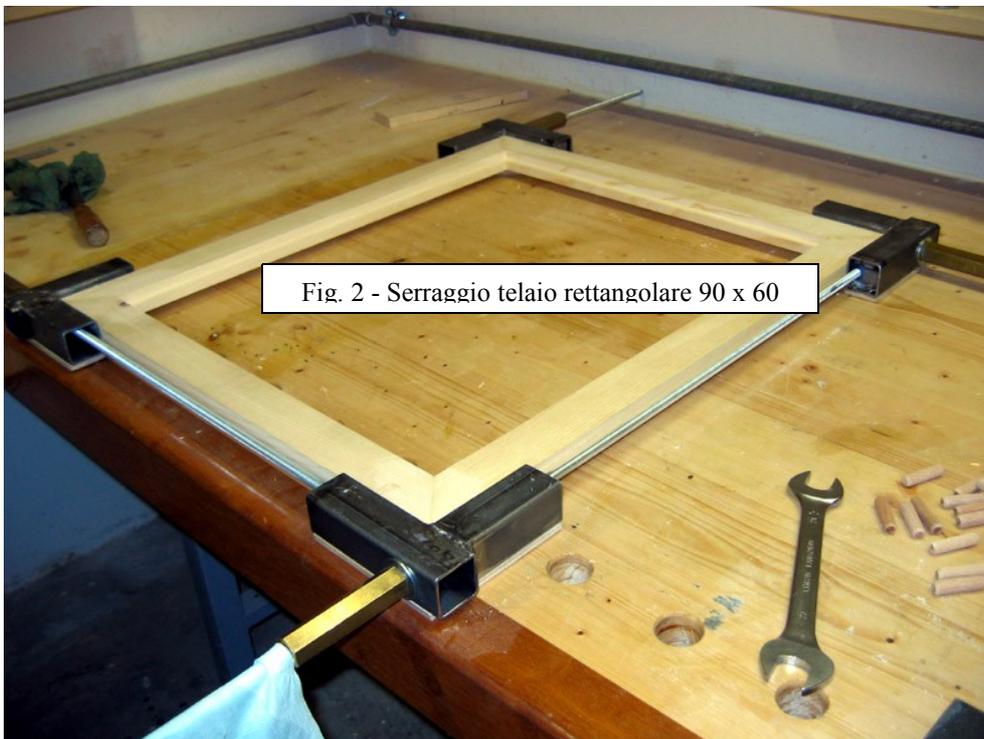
Serraggio telaio rettangolare 90 x 60
